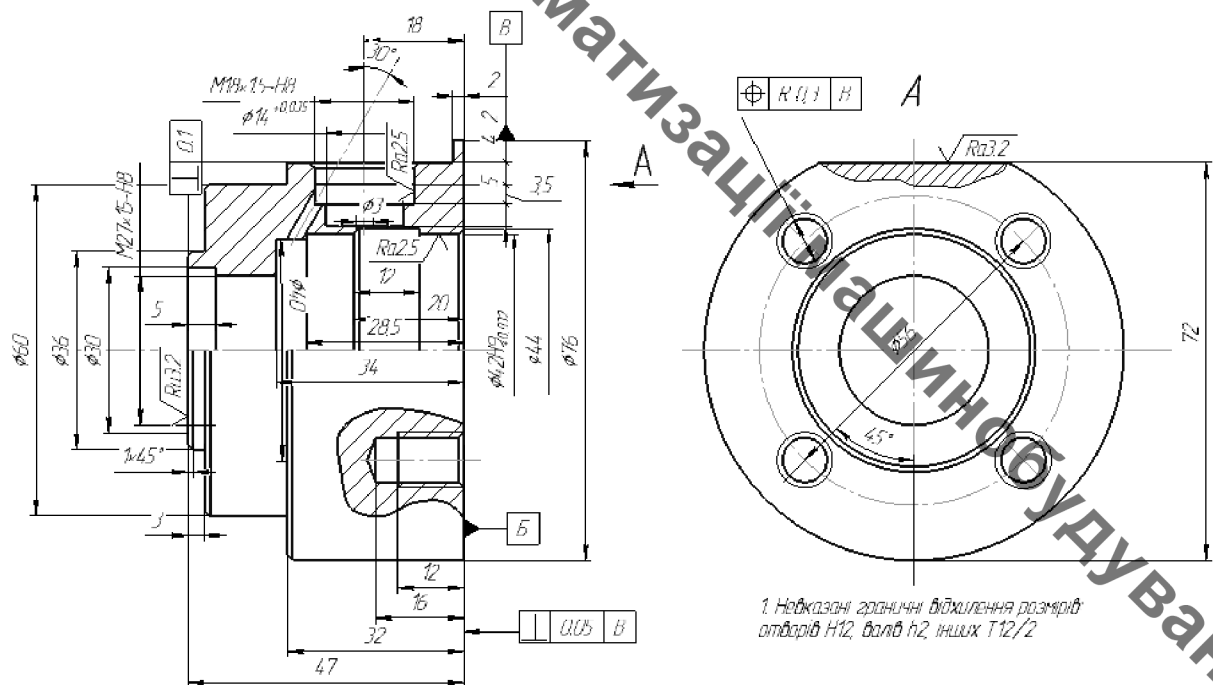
Ескіз деталі «Корпус клапана»
